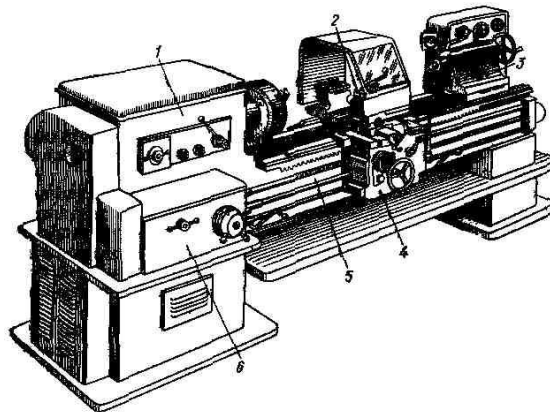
Загальний вигляд токарно-гвинторізного верстата моделі 1К62
